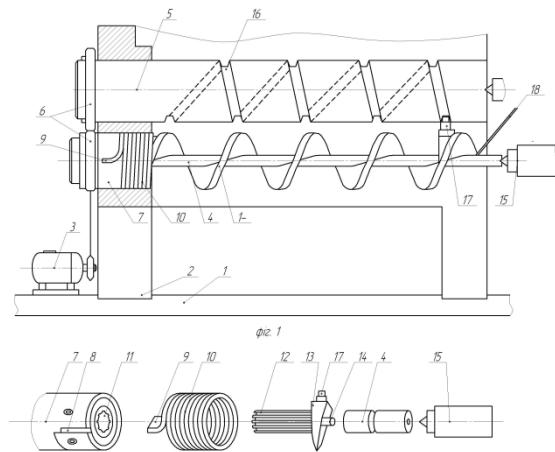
Пристрій для калібрування і виготовлення гвинтових робочих органів зі змінними кроками виконано
